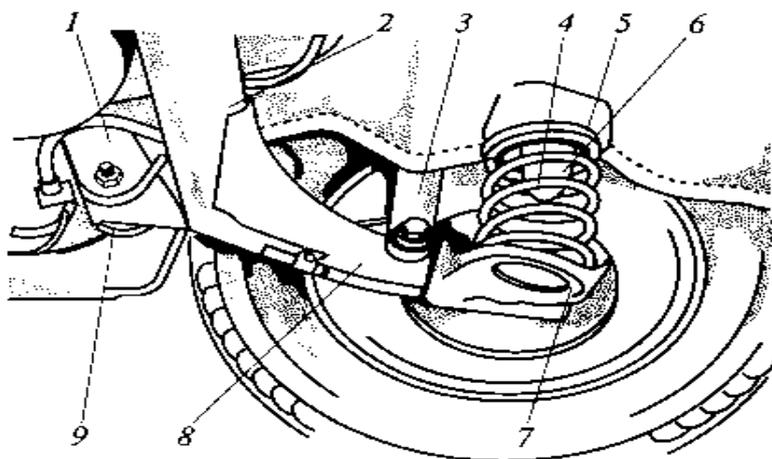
Независимая подвеска правого заднего колеса: 1 — кронштейн; 2 — соединитель рычага; 3 — амортизатор; 4 — пружина подвески; 5 — изолирующая подушка; 6 — буфер хода сжатия; 7 — опорная чашка пружины подвески; 8 — рычаг подвески; 9 — резинометаллический шарнир
